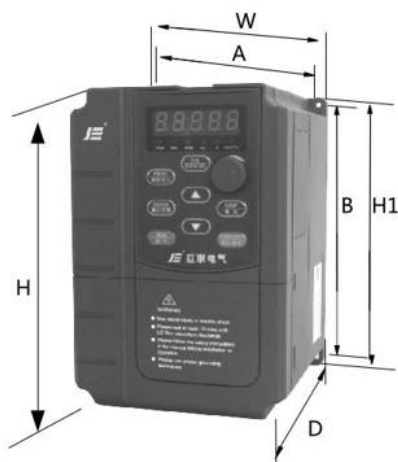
JL910系列 塑胶结构外型尺寸及安装尺寸示意图
